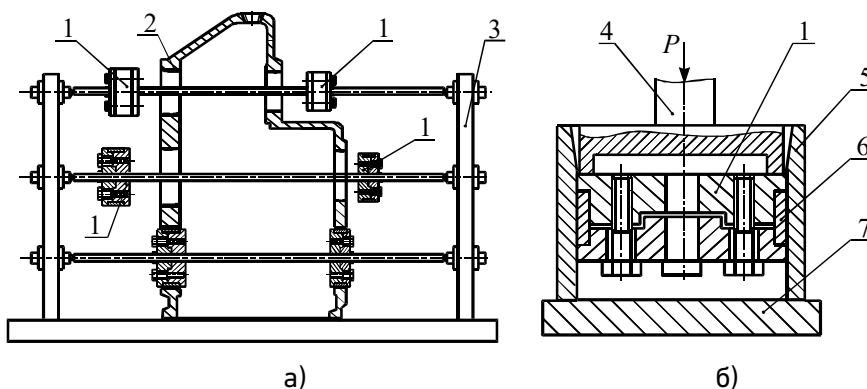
Схема центрувального пристрою (а) та обтискача втулки (б):
